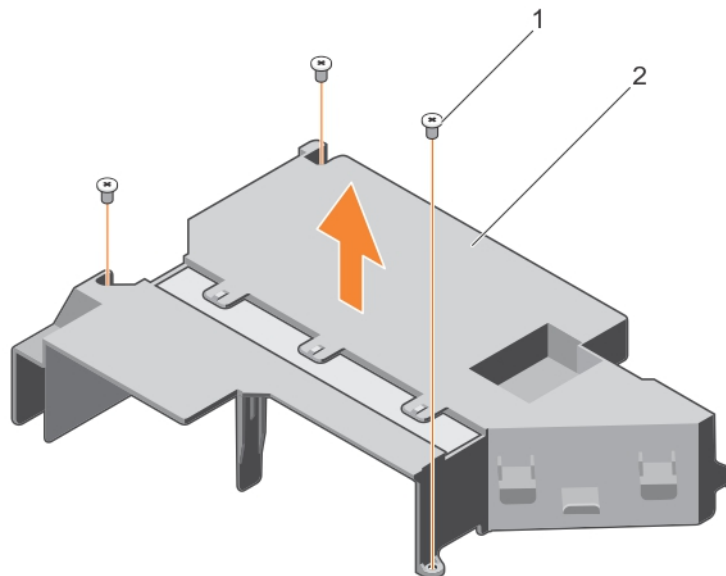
Entfernen und Einsetzen des Kühlgehäuses.
